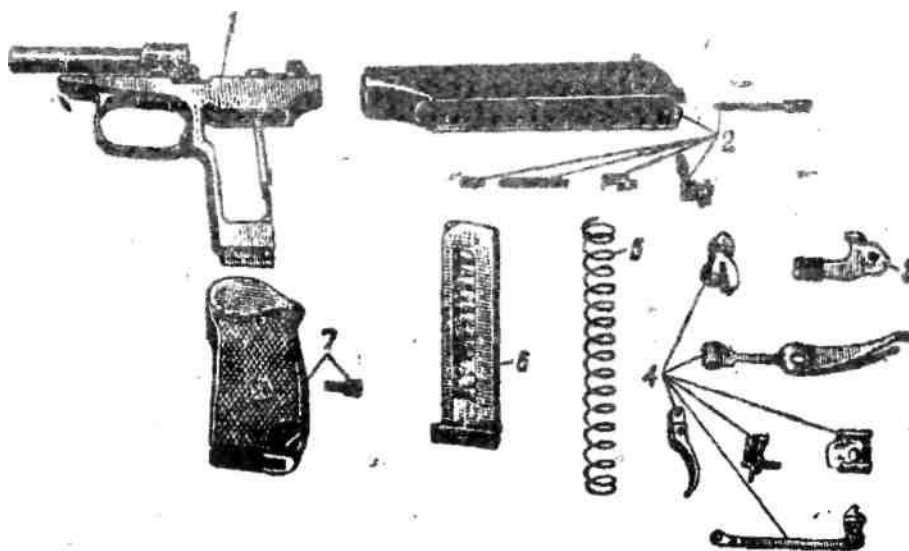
Основные части и механизмы пистолета 1 — рамка со стволом и спусковой скобой; 2 — затвор с ударником, выбрасывателем и предохранителем; 3 — затворная задержка; 4 — части ударно-спускового механизма; 5 — возвратная пружина; 6 — магазин; 7 — рукоятка с винтом
